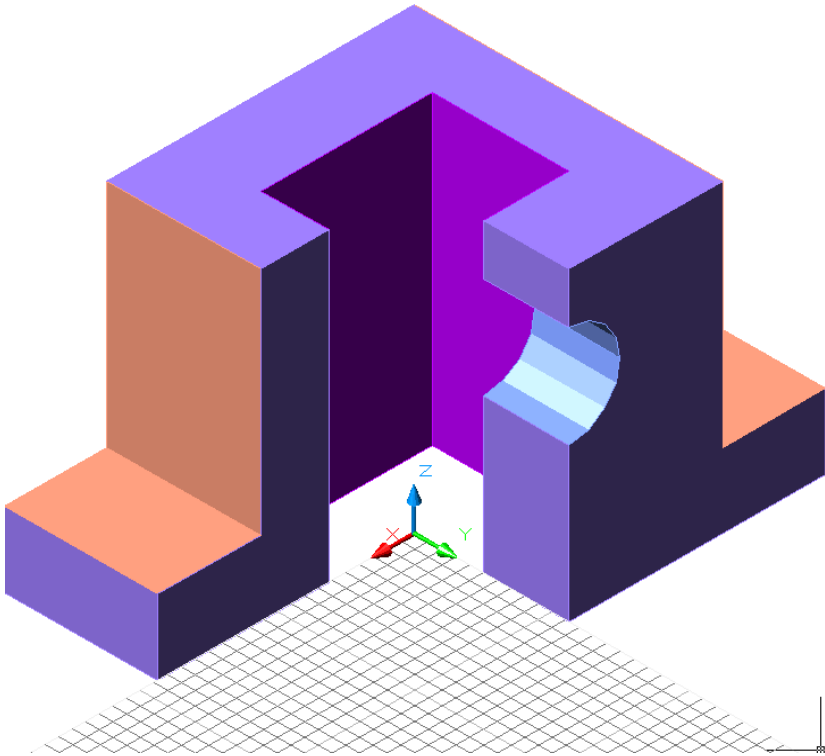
Деталь з вирізом 1/4 частини
